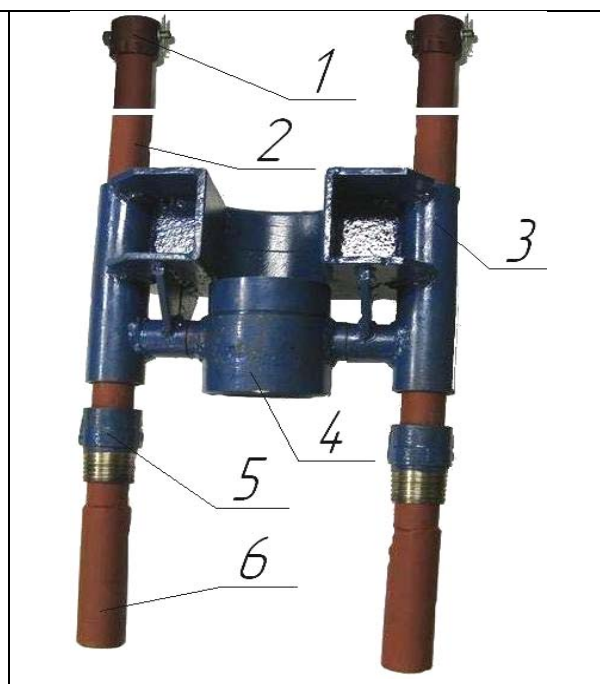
Направляющий узел в сборе: 1 - съемный ограничитель; 2 - направляющая стойка 3 - направляющая каретка; 4 - поворотная воронка; 5 - монтажная втулка; 6 - опорный патрубок
